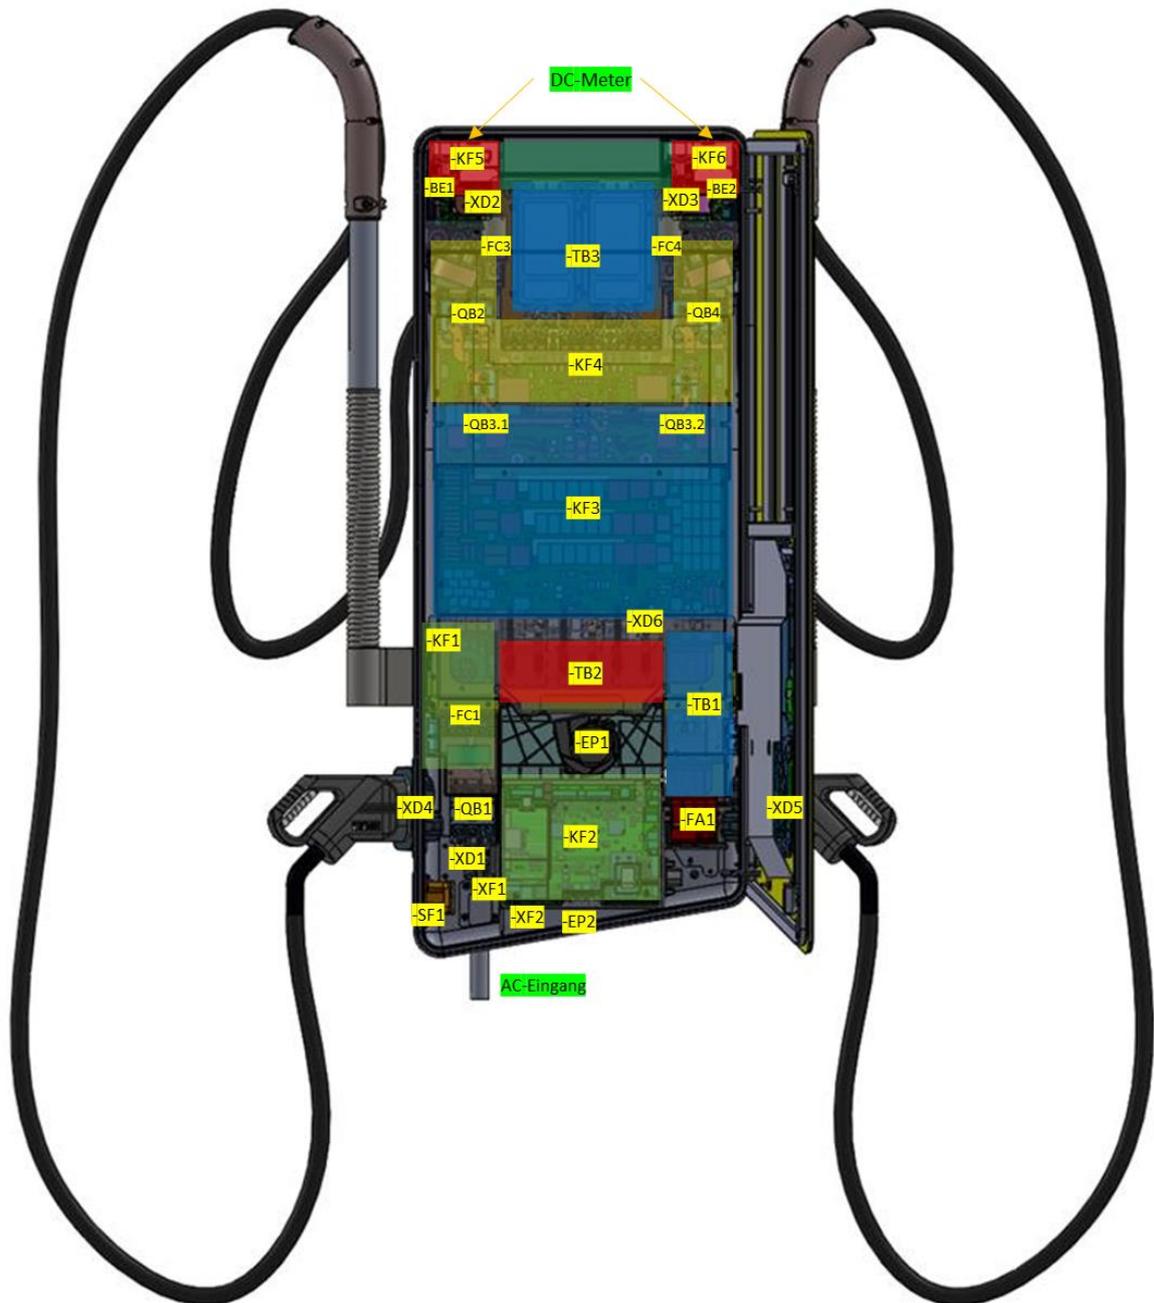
Innenansicht HYC_50 (Innenansicht Draufsicht mit 2x DC-Ladekabeln)
